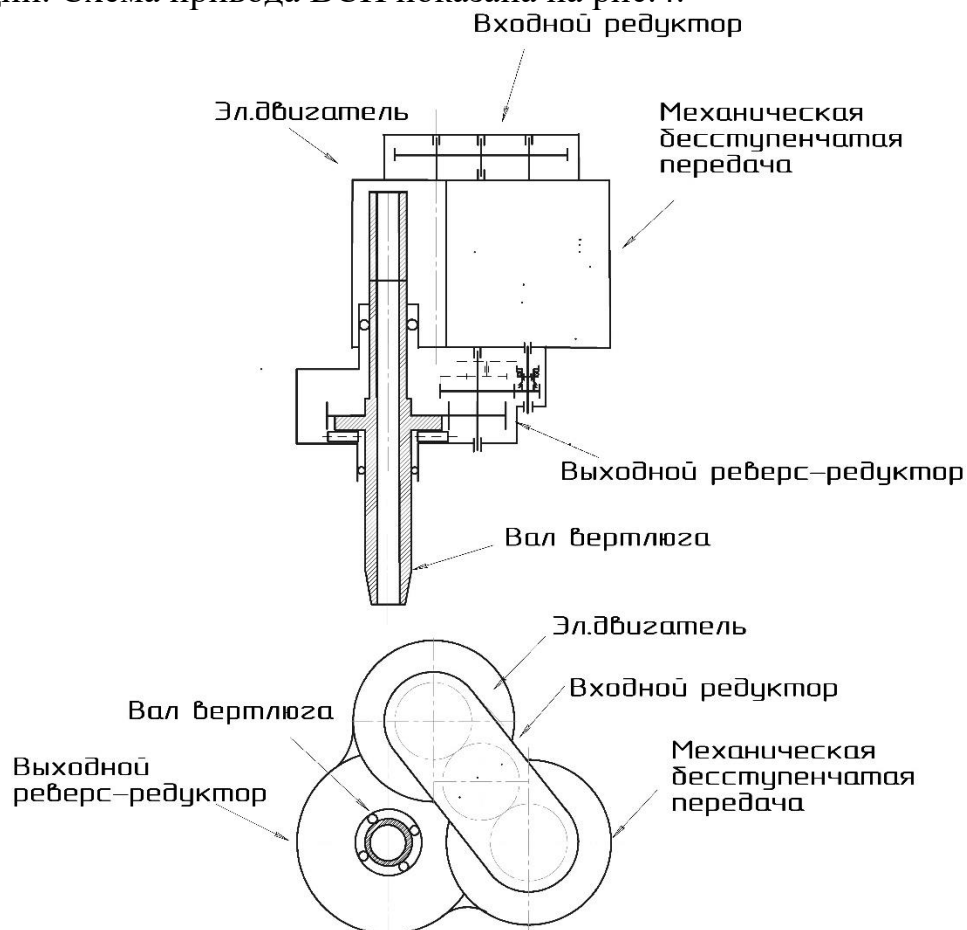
Кинематическая схема привода с механической бесступенчатой передачей.
